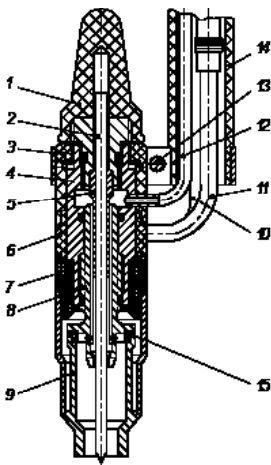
Schema constructivă a capului de sudare robotizată WIG
